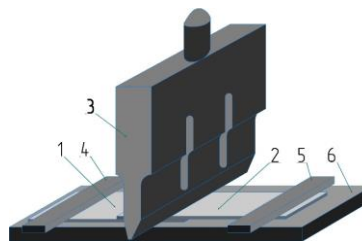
Схема соединения образцов ультразвуковой сваркой: 1, 2 – свариваемые образцы, 3 – ультразвуковой излучатель, 4, 5 – прижимные планки, 6 – опора
